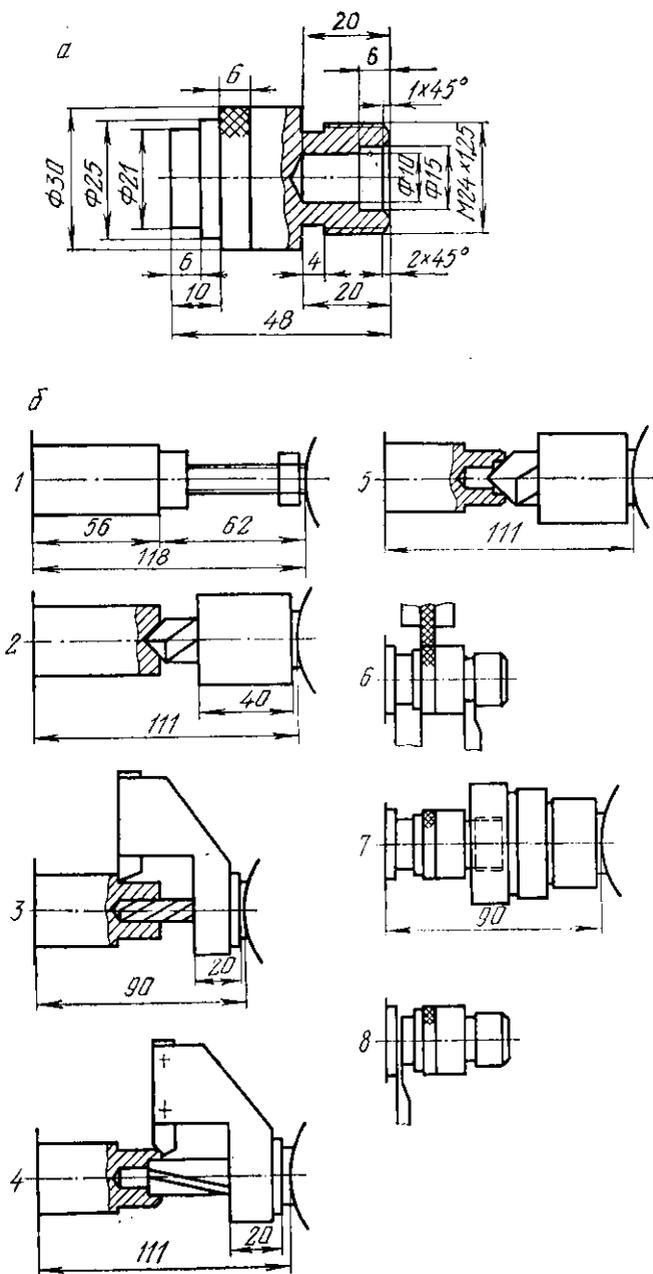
Рабочий чертёж пробки и схема ее обработки
